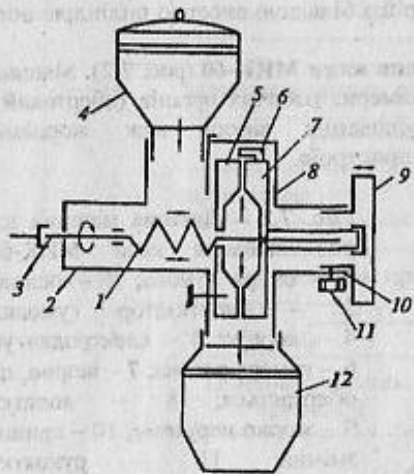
Механізм для розмелювання кави МКК-120: 1 – шнек; 2 – корпус; 3 – вал робочий; 4 – бункер завантажувальний; 5 – жорно нерухоме; 6 – лопатка; 7 – жорно, що обертається; 8 – кришка; 9 – гайка; 10 – хвостик; 11 – гвинт; 12 – бункер приймальний
